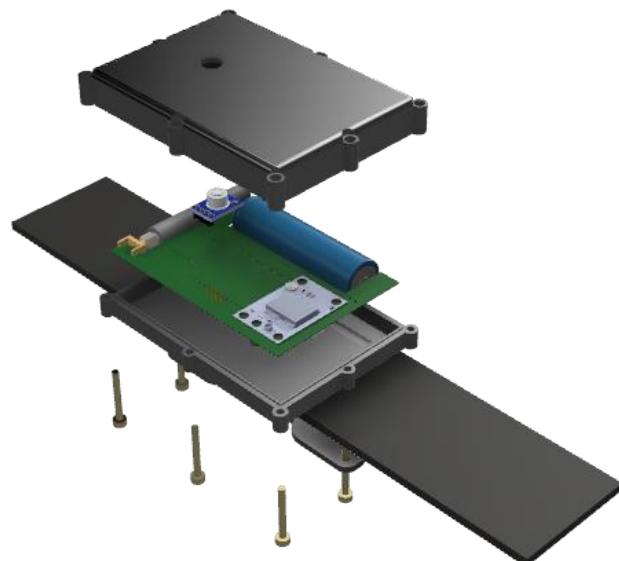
Ensamblaje del dispositivo remoto o nodo final [Elaboración Propia].
